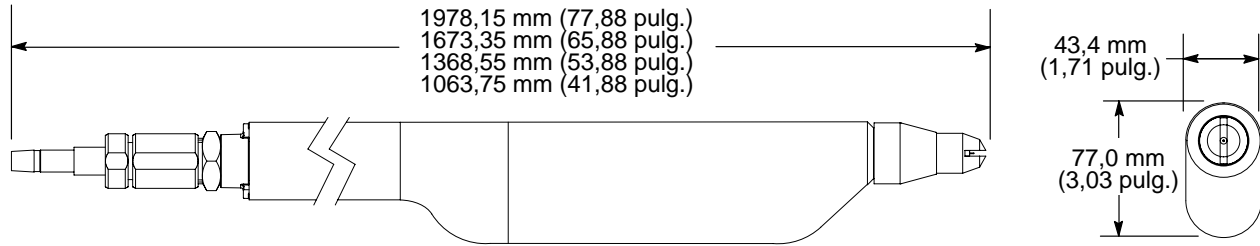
Dimensiones de la pistola para montaje en tubo
